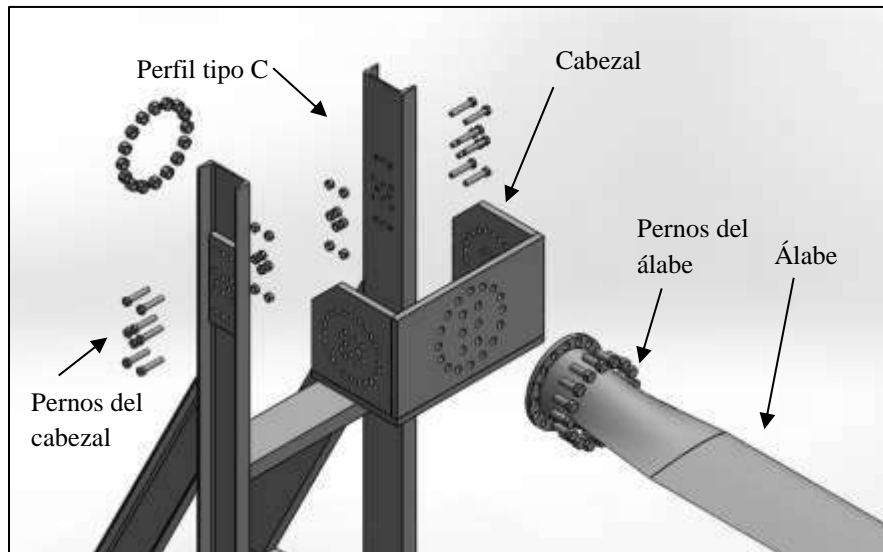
Vista explosionada del cabezal 4. Fuente: SOLIDWORKS 2017.
